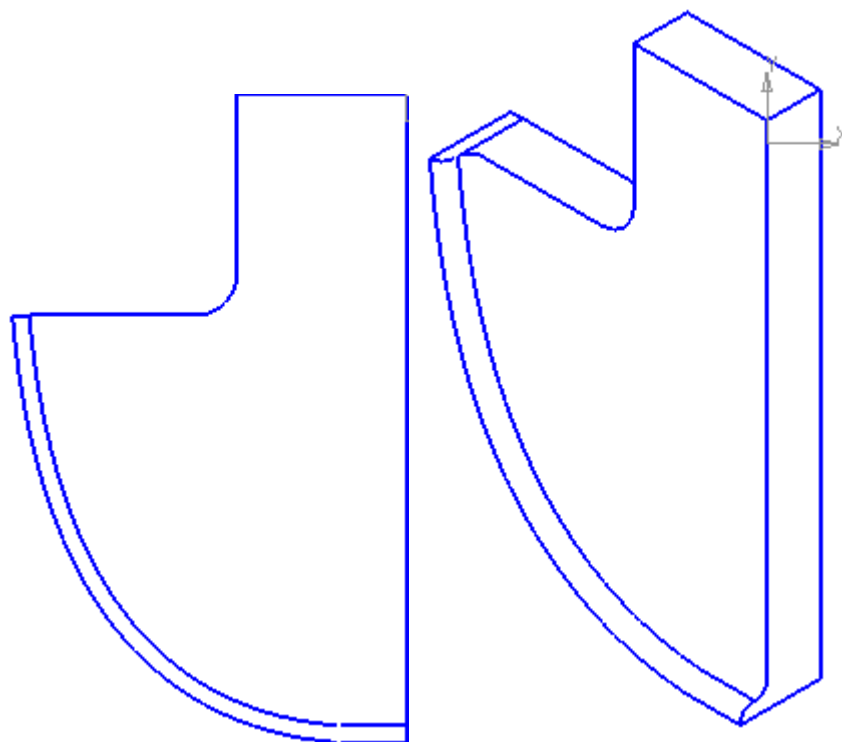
Лопать для перемішування в зоні сферичної частини котла
